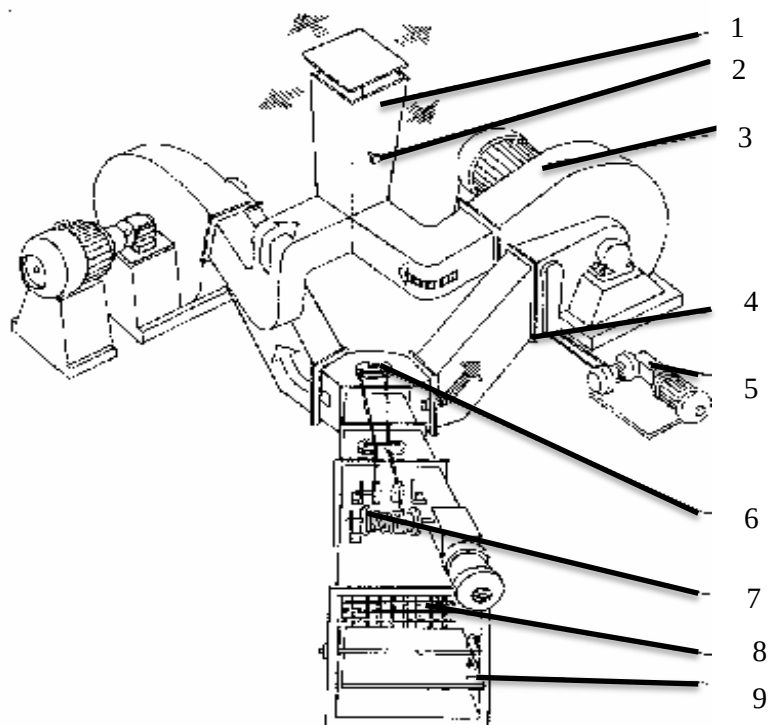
Установка вентиляторная центробежная газоотсасывающая
